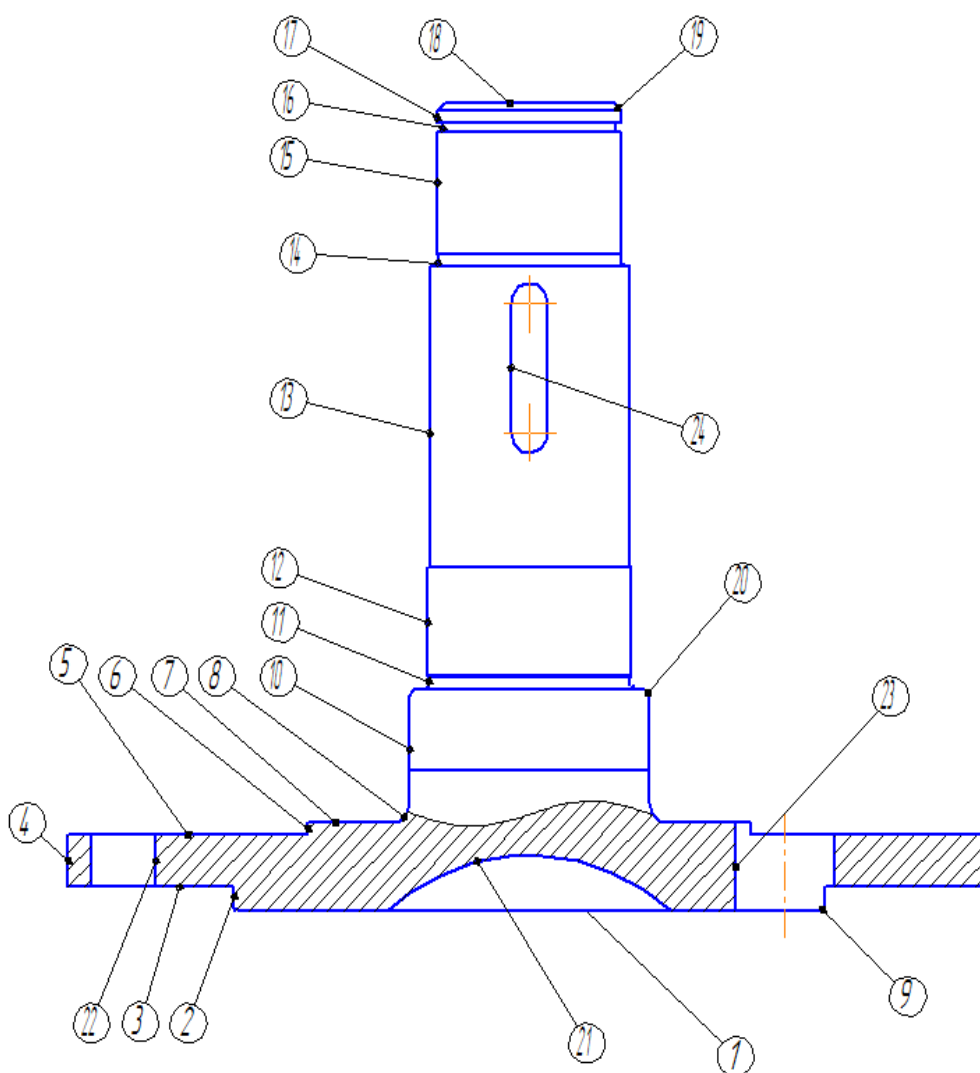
Эскиз детали с номерами обрабатываемых поверхностей
